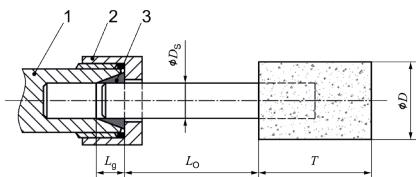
Inspänningslängd från spännc Chuck och spännyhsan
